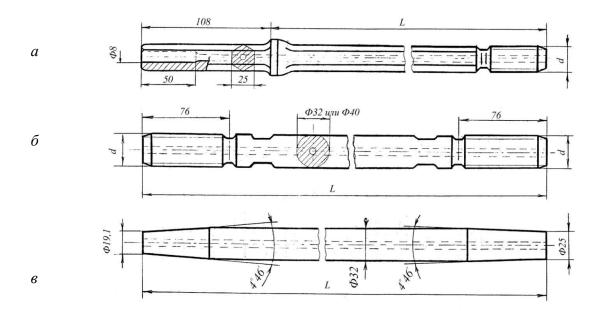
Штанги (буры) перфораторов и бурильных головок а — штанга шестигранная с резьбовым креплением коронки; б — штанга круглая с резьбой; в — штанга круглая с конусами
